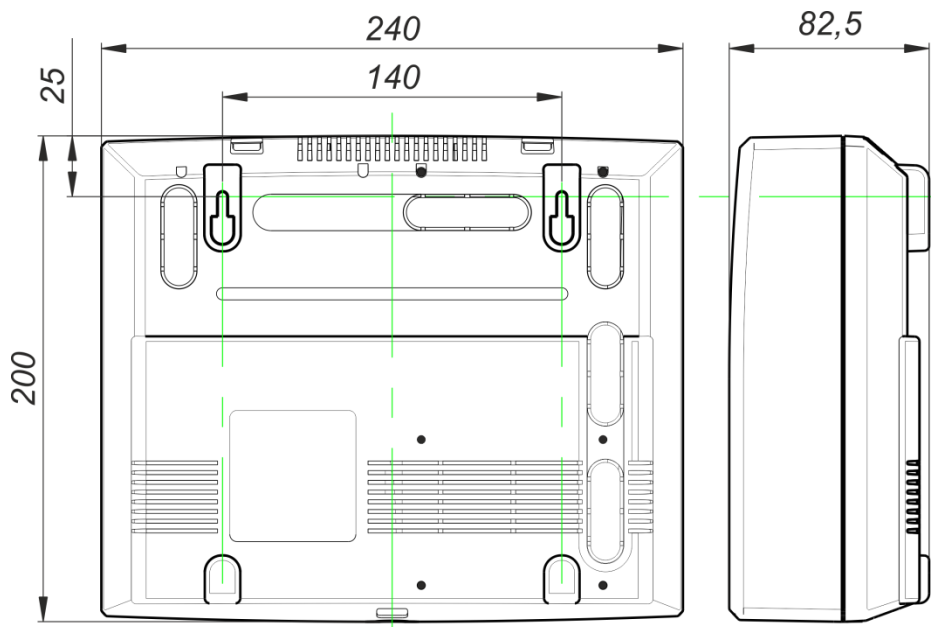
Габаритные и установочные размеры приборов ВЕРСЕТ 2(4,8).
